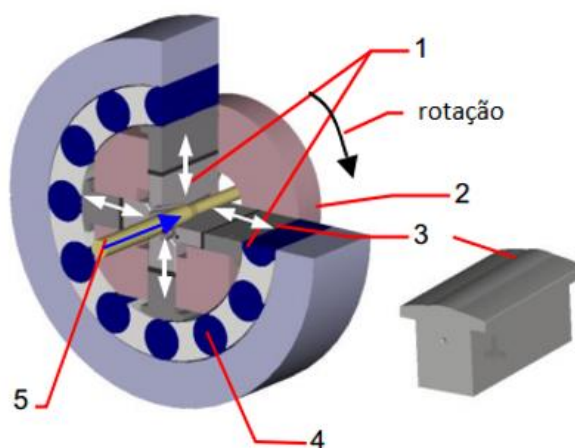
Desenho esquemático do cabeçote de forjamento rotativo mostrando seus componentes [61].
